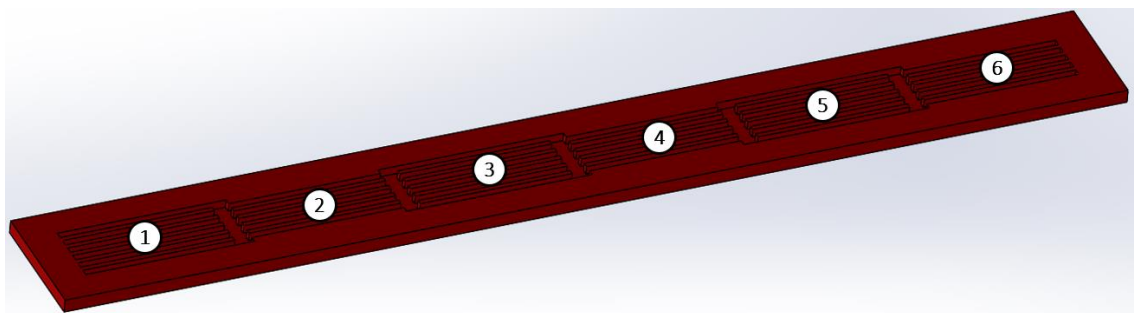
Plato1 del Hotplate UPNA. Diseño en SOLIDWORKS.
